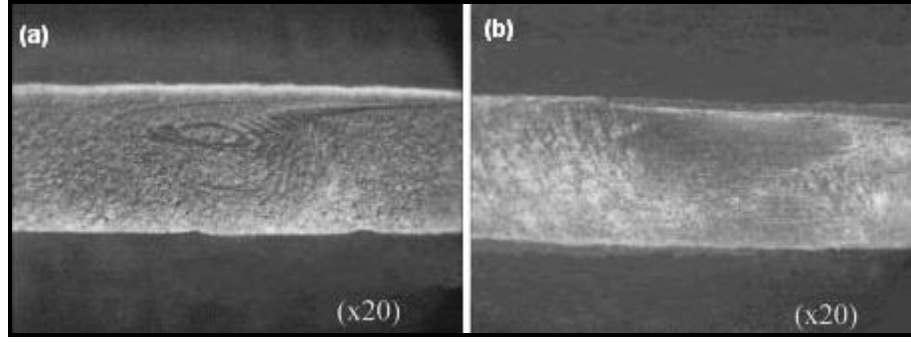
2050 devir/dakika takım dönme hızında ve 112 mm/dakika kaynak hızlarında gerçekleştirilen birleştirmenin, kaynak bölgesi makro ve mikroyapı bölgeleri [133]
